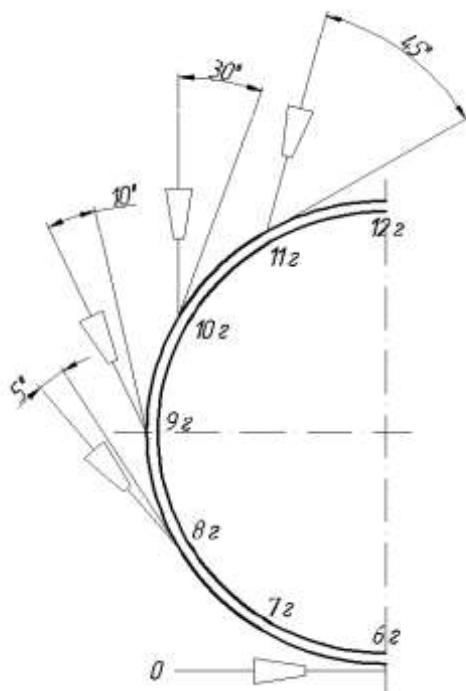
Схема зміни кута нахилу порошкового дроту при зварюванні неповоротного стика
